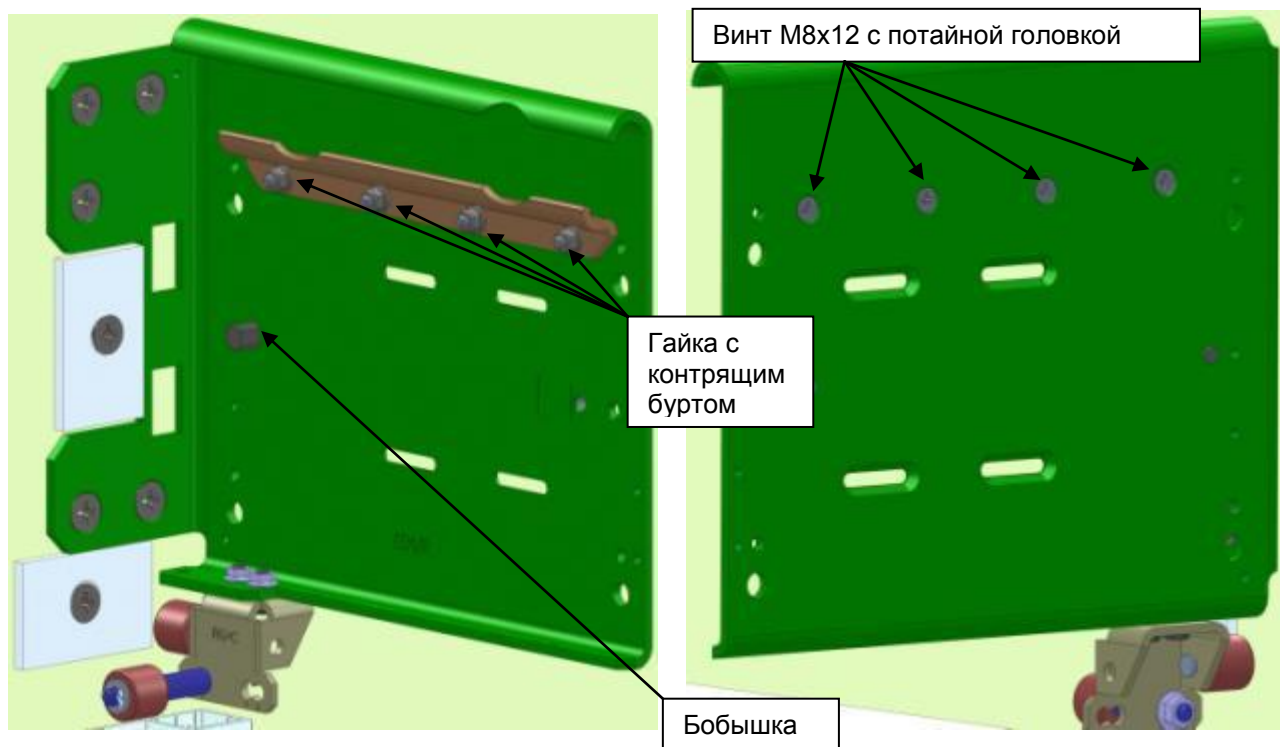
Крепление направляющей каретки RC360/С на консоли ССМ
